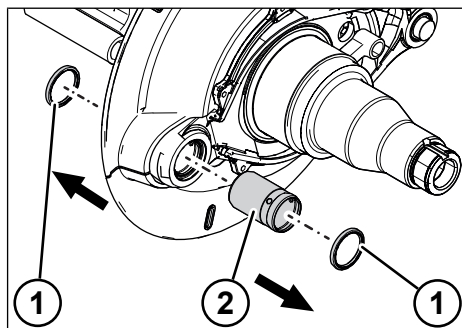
Retirer le coussinet de palier de came du support de frein
